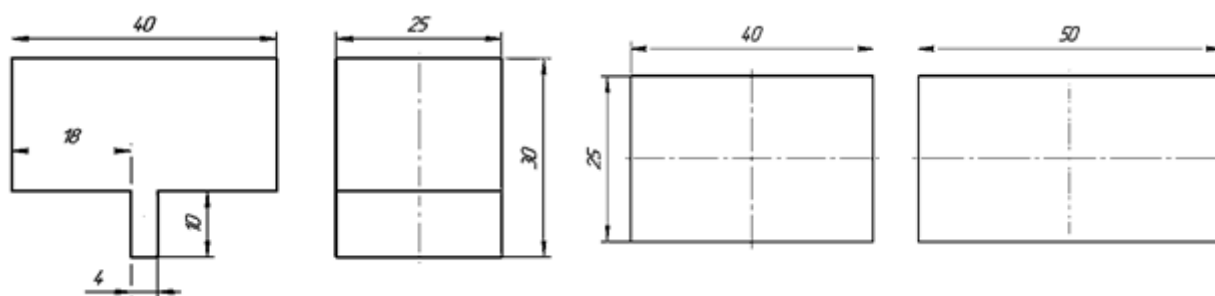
Форма и размеры моделей пуансона и заготовки для проведения моделирования процесса прессования
